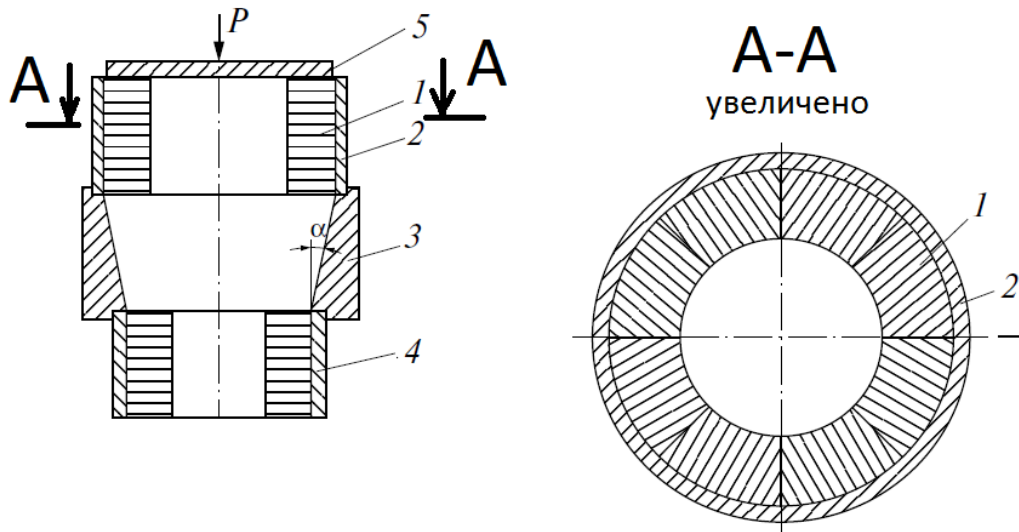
Схема запрессовки подшипника: *1* – сегменты; *2* – вспомогательная обойма; *3* – конус; *4* – окончательная обойма; *5* – пуансон
